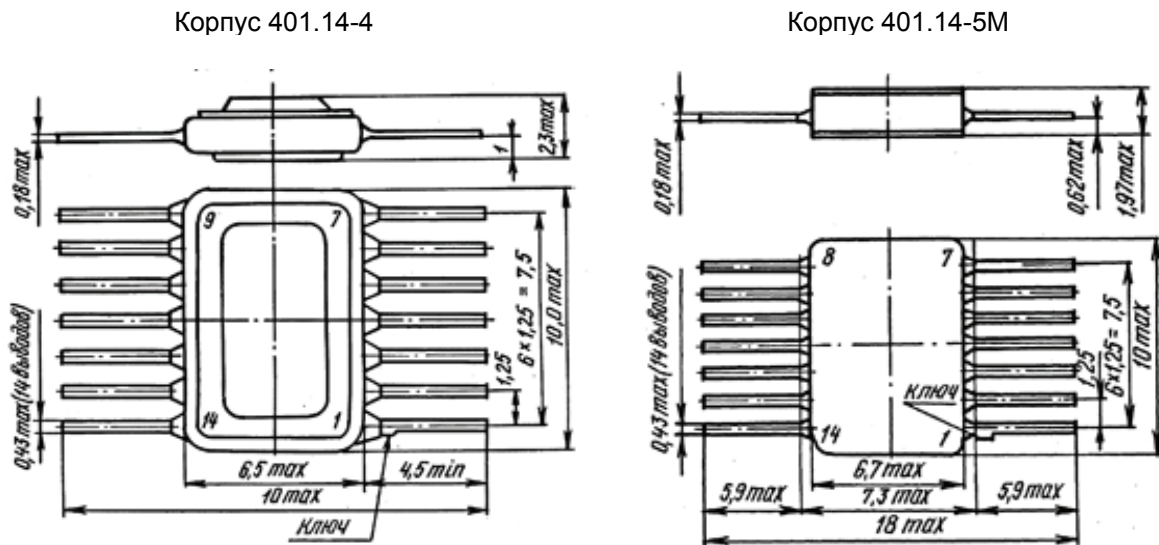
Габаритные чертежи корпусов 401.14-4 и 401.14-5М
